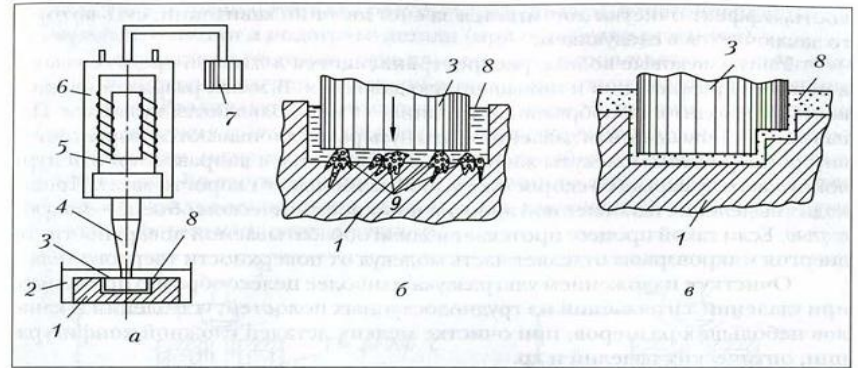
Ультразвуковая размерная обработка: *а* — принципиальная схема; *б* — схема съема материала при ультразвуковом прошивании; *в* — схема воспроизведения профиля инструмента в заготовке: 1 — заготовка; 2 — ванна; 3 — инструмент; 4 — волновод-концентратор (трансформатор амплитуды); 5 — преобразователь; 6 — корпус преобразователя; 7 — генератор тока ультразвуковой частоты; 8 — зазор, заполненный суспензией абразива; 9 — частички абразива (зерна)
